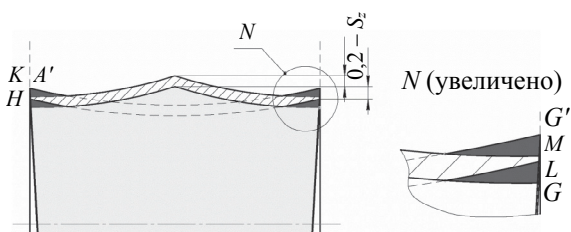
Схема формирования пропила дисковой твердосплавной пилой с плоско-треугольным профилем зубьев
